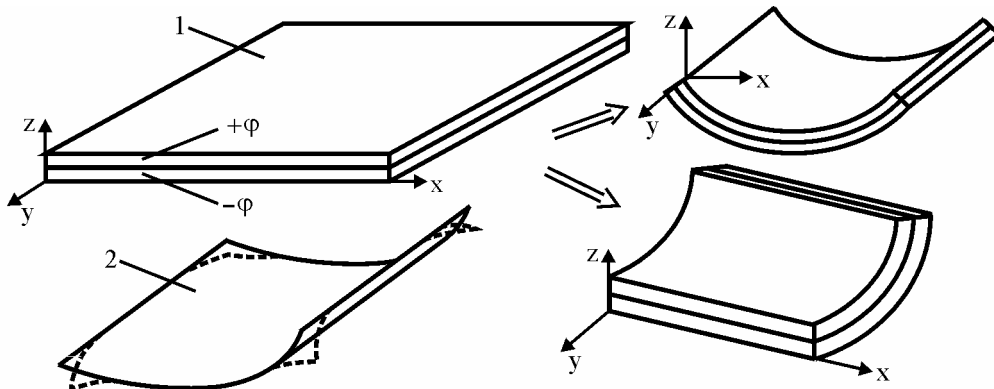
Варианты коробления пластин из КМ: 1 – коробление с образованием цилиндрической поверхности; 2 – проявление краевого эффекта (загиб углов профиля)
